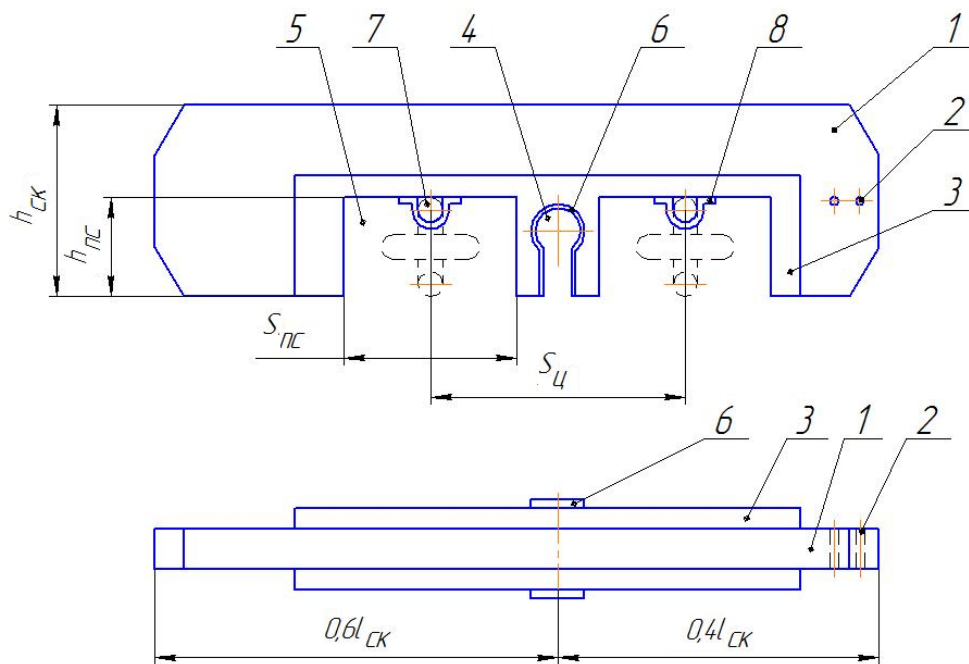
Конструктивная схема скребка ЗЗСК
